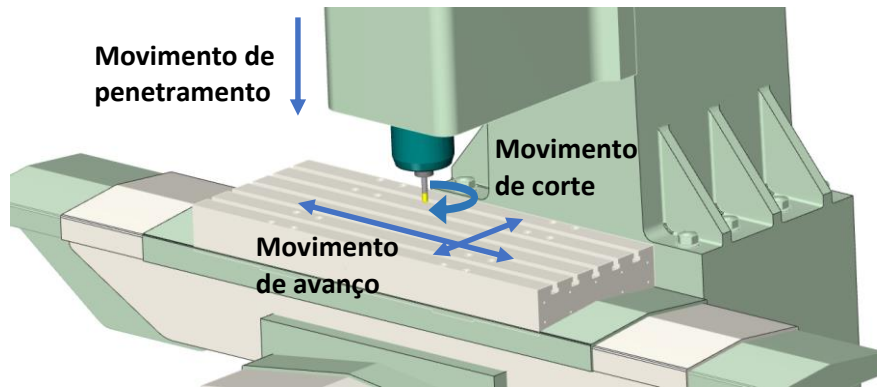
Movimentos realizados por uma fresadora ou centro de maquinagem
